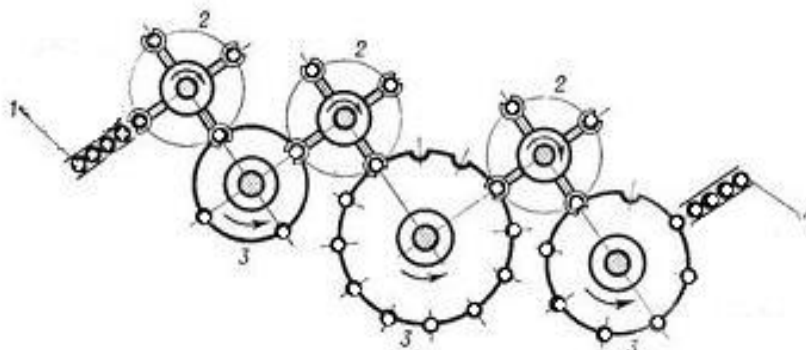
Схема роторной линии: 1 — питающие устройства; 2 — транспортный ротор; 3 — рабочий ротор; 4 — приёмные устройства.
